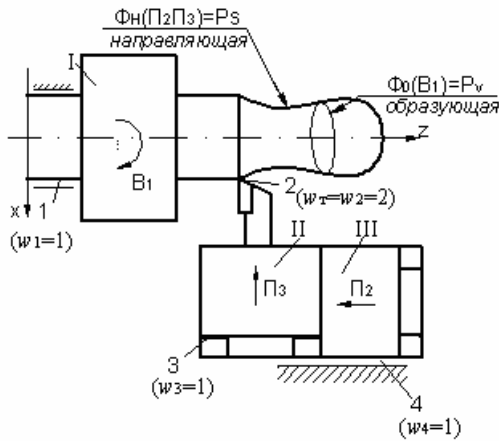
Токарный четырехзвенный технологический механизм фасонного точения резцом (I – шпиндель с изделием; II – поперечные салазки с резцом; III – продольные салазки суппорта)
